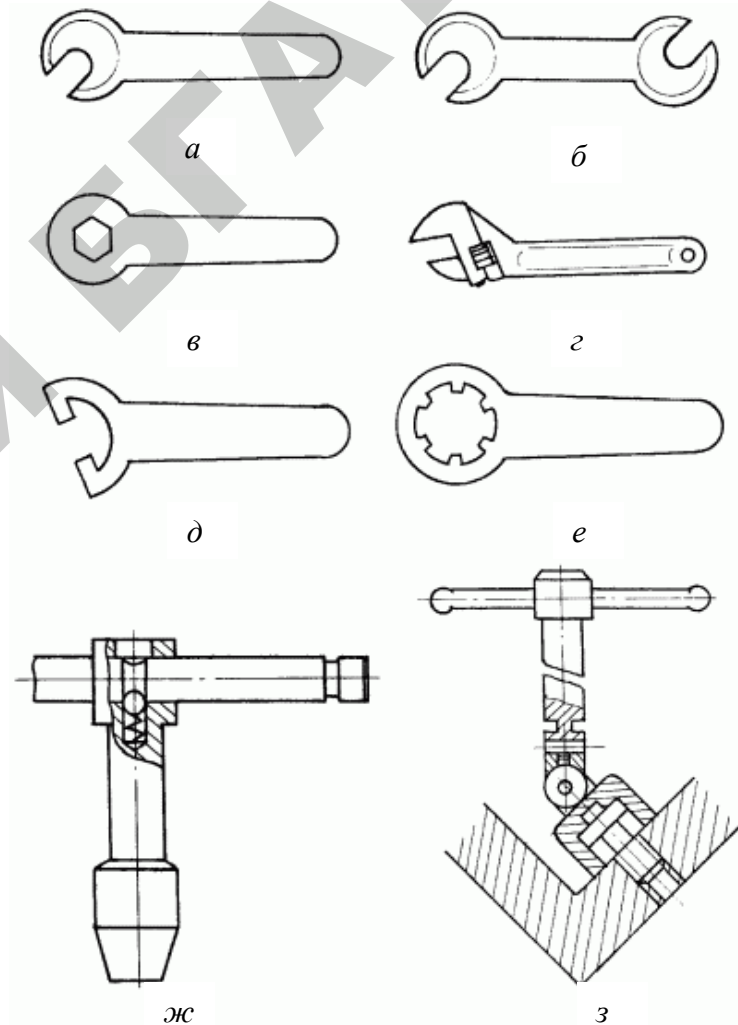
Ручной инструмент для сборки резьбовых соединений. Ключи: *a* – односторонний; *б* – двухсторонний; *в* – накладной; *г* – разводной; *д* – накидной открытый для круглых гаек; *е* – накидной закрытый для круглых гаек; *ж* – торцовый; *з* – торцовый шарнирный
